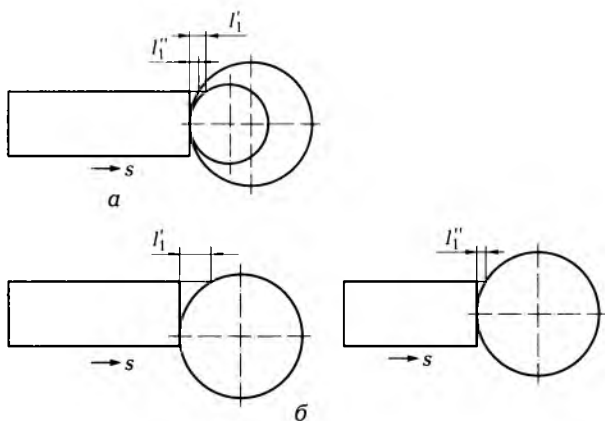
Схемы уменьшения величины добавки на вход режущего инструмента при фрезеровании за счет увеличения диаметра фрезы (а) и установки оси фрезы по оси симметрии детали (б)
